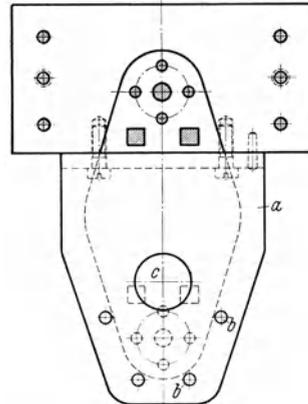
Offene Einlage mit Führungsstiften an einem Auflageblech.
